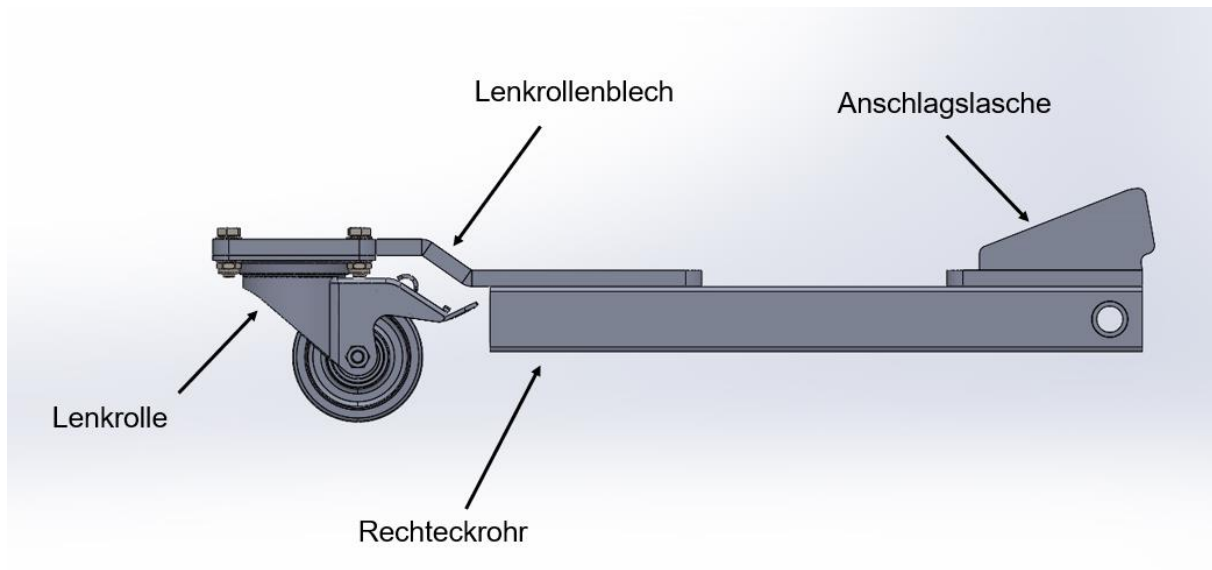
CAD-Konstruktion Schwenkarm Seitenansicht
